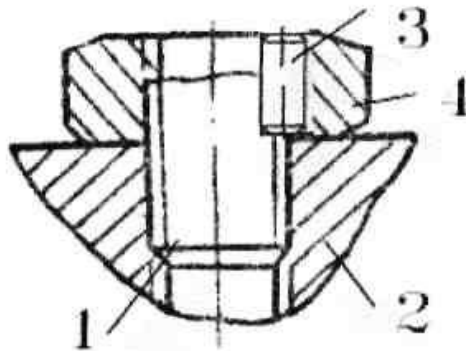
Гайка з циліндричним штифтом: 1-шпилька; 2- деталь; 3- штифт; 4-гайка
